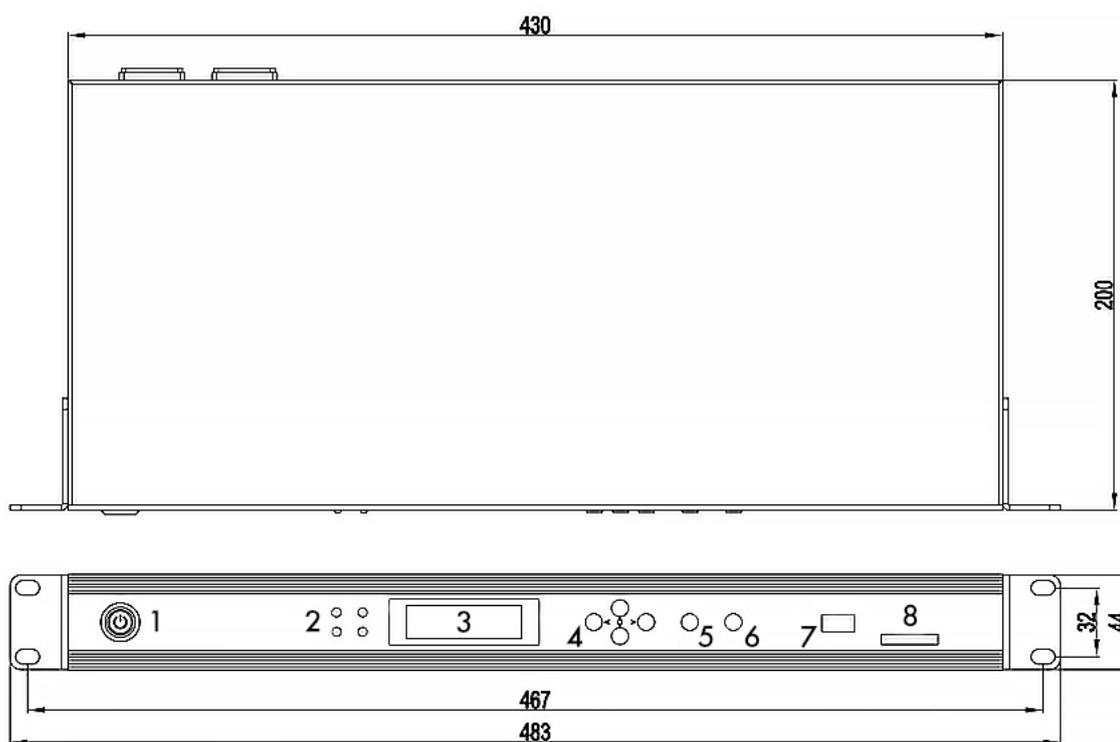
Вид сверху и спереди: габаритные размеры. Цифрами обозначены:
